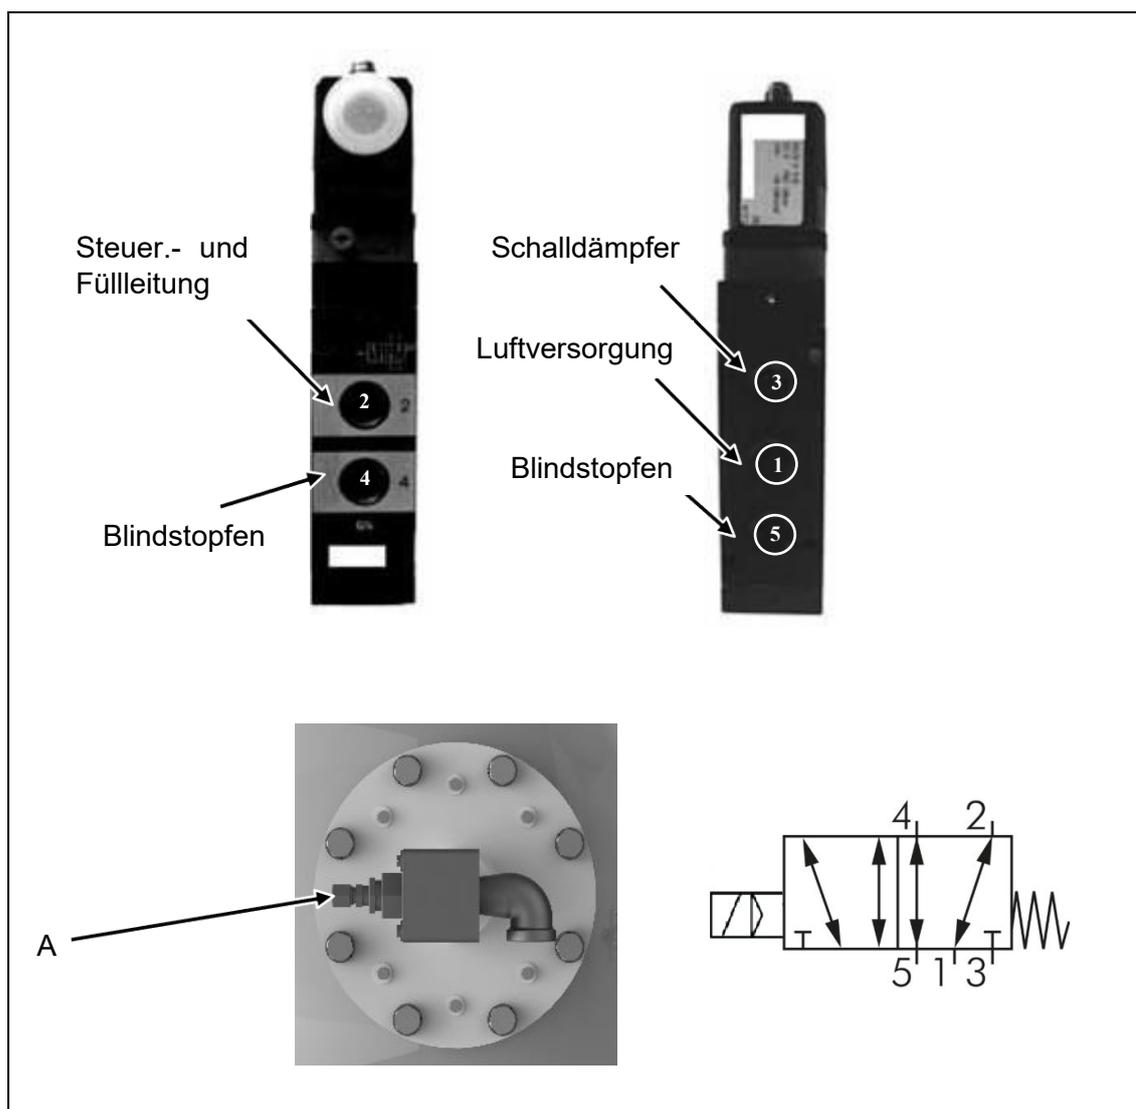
Pneumatischer Anschluss des 5/2-Wege Magnetventils
